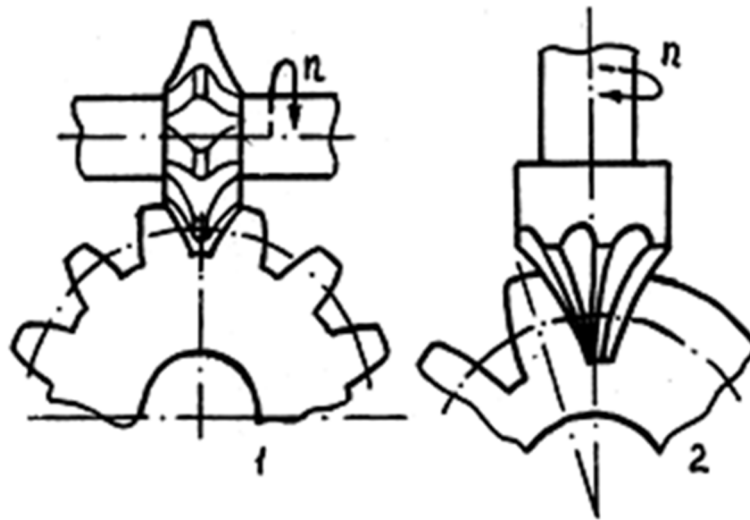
Схема фрезерування зубців за методом копіювання:
